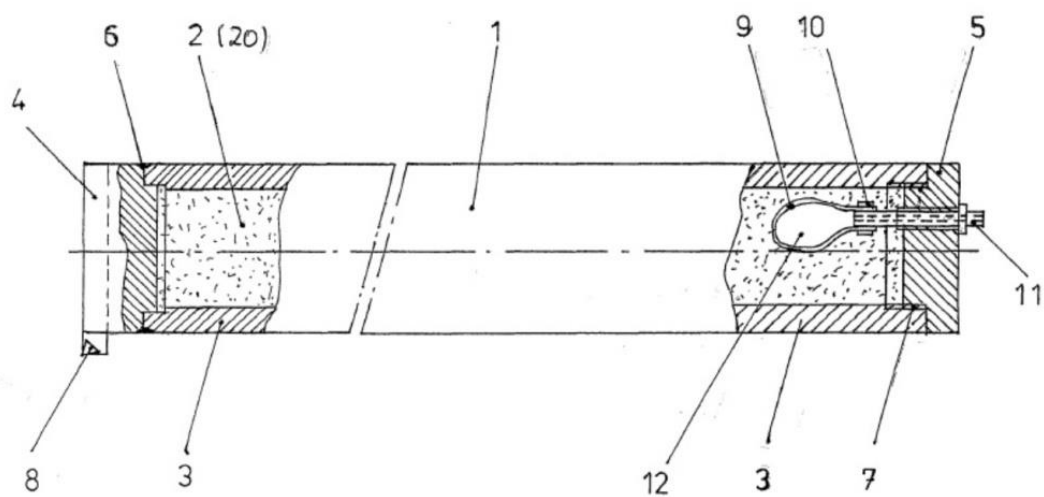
Демпфуючий інструмент. Вигляд 1.
